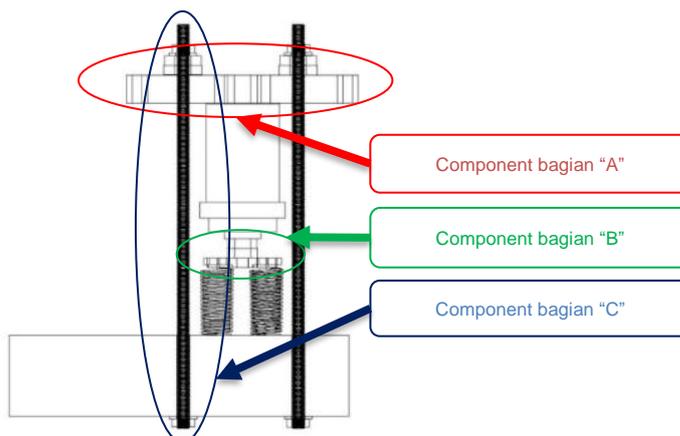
Design Special service tool remove dan install valve spring dengan 4 valve spring sekaligus
